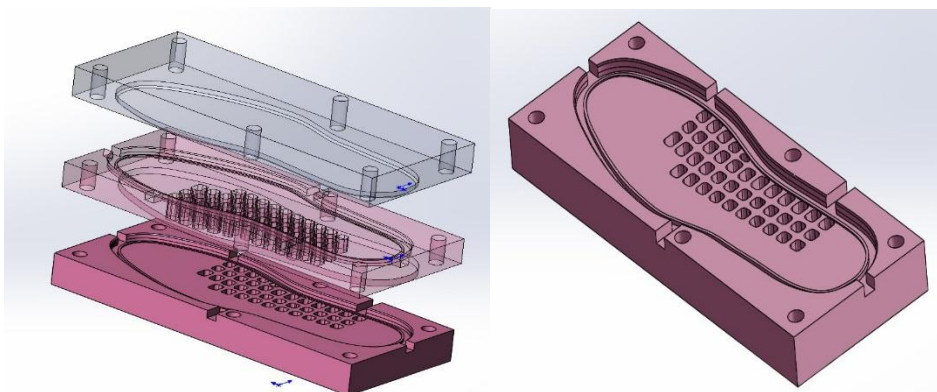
А Модель прототипа изделия. В Оригинальная форма для отливки стельки
